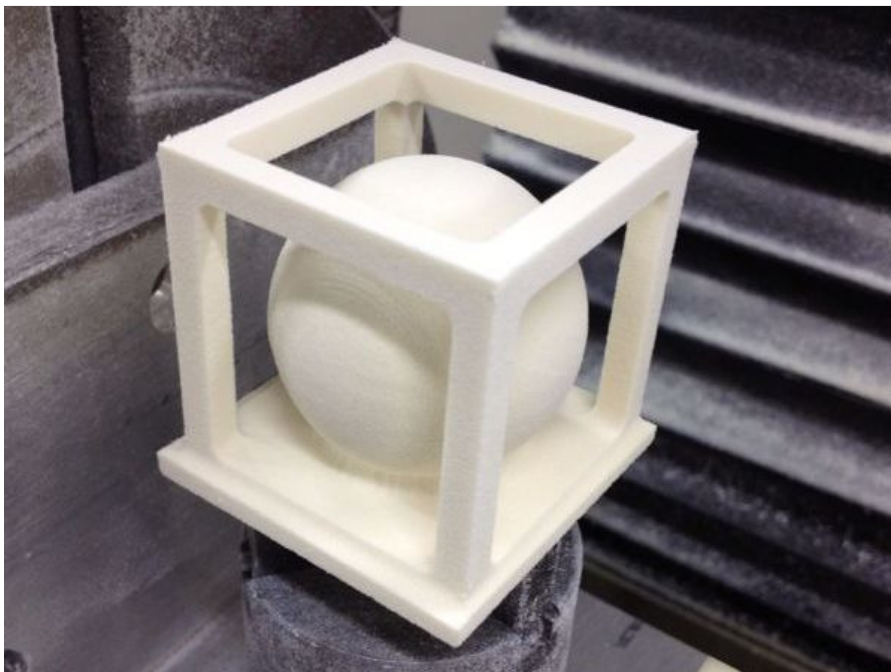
Usinagem final em fresadora Tormach PCNC 1100 com cinco eixos
